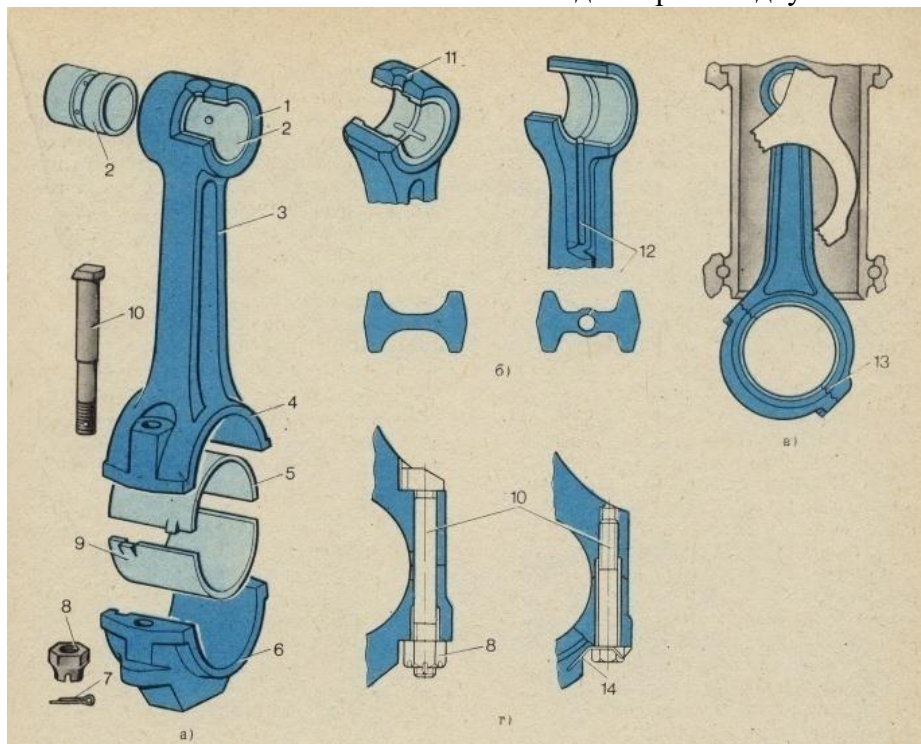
Конструкции шатунов: а - детали шатуна, б - сечения стержня шатуна и подвод масла к поршневому пальцу, в - косой разъем нижней головки шатуна, г - способы фиксации крышки нижней головки шатунов; 1 - верхняя головка шатуна, 2 - втулка верхней головки шатуна, 3 - стержень шатуна, 4 - нижняя головка шатуна, 5 - вкладыш шатунного подшипника, 6 - крышка нижней головки шатуна, 7 - шплинт, 8 - корончатая гайка, 9 - фиксирующий усик вкладыша, 10 - шатунный болт, 11 - отверстие для подвода масла, 12 - канал для подвода масла в теле шатуна, 13 - треугольные шлицы в стыке крышки с нижней головкой шатуна, 14 - стопорная шайба.
